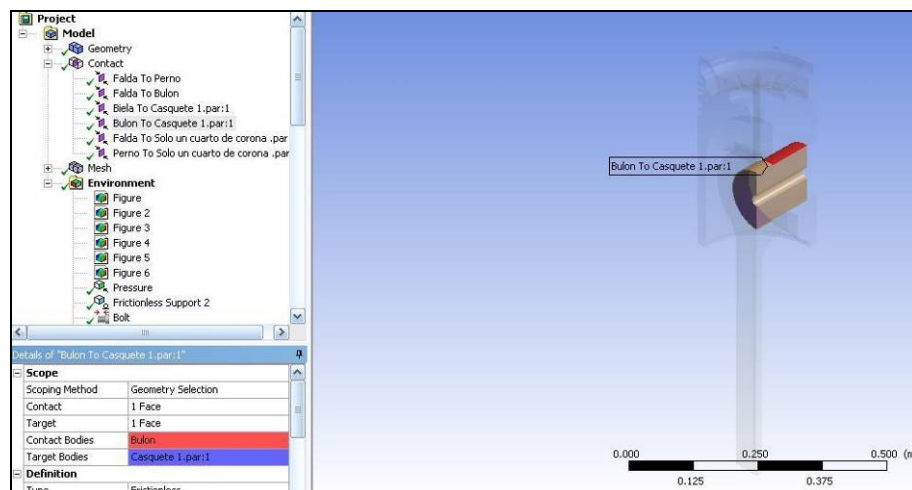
Contacto tipo sin fricción entre Bulón - Casquete.
